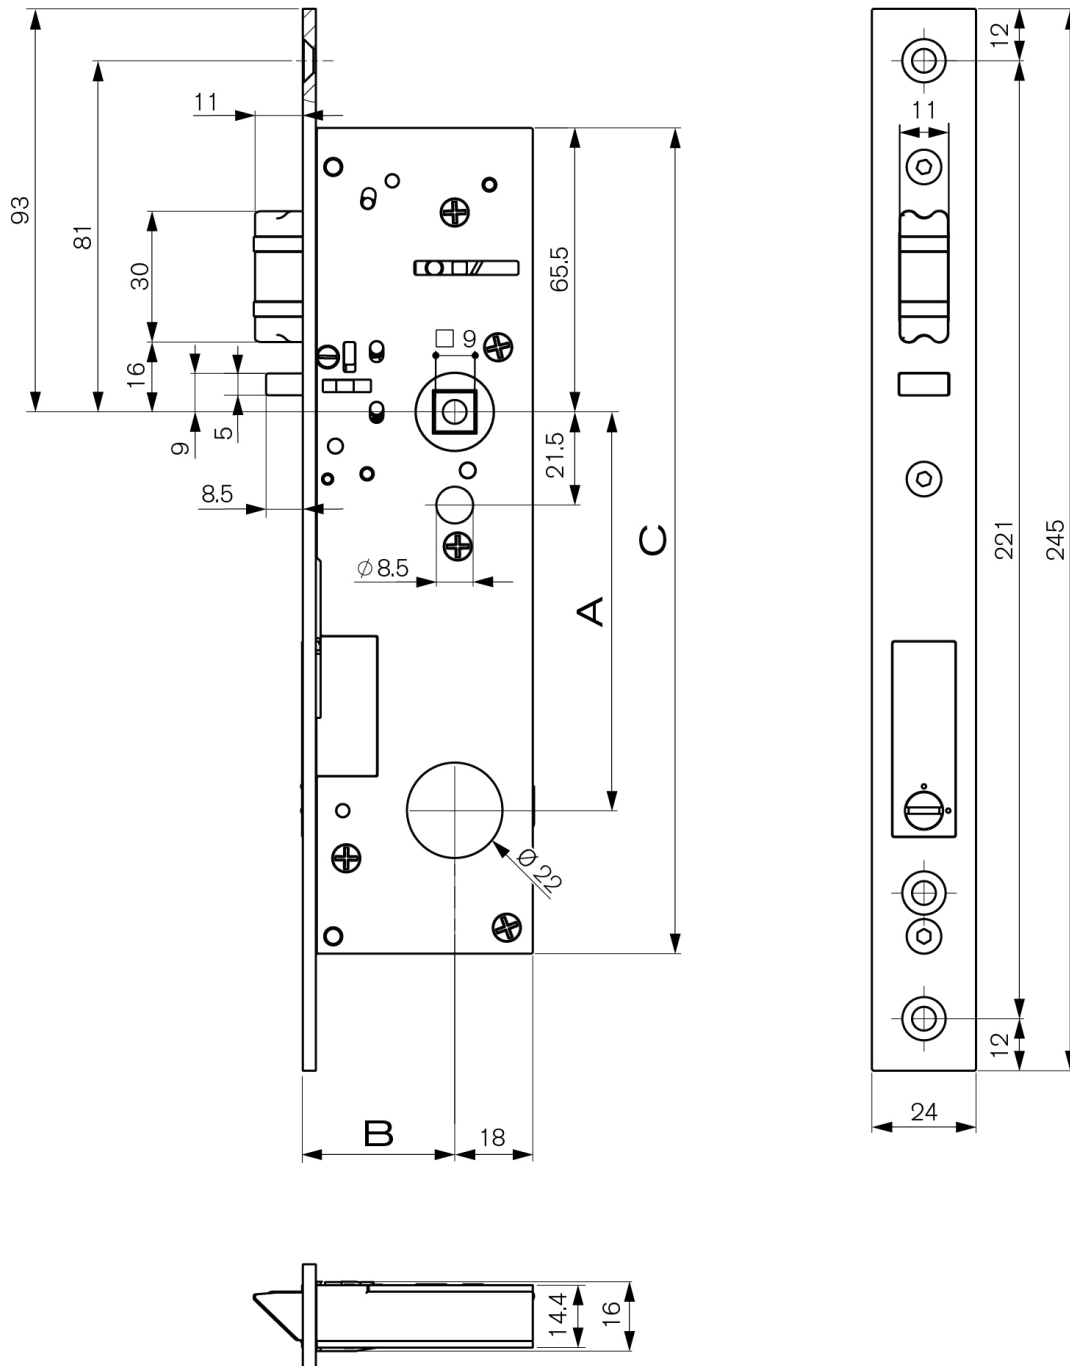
Abmessungen für Schlossinstallation – Rundzylinder 94
